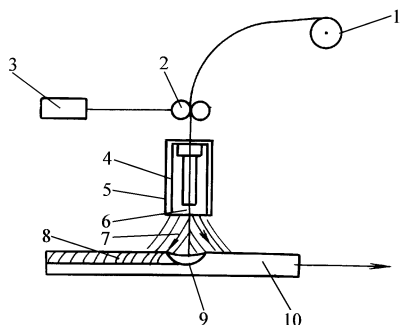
二氧化碳气体保护焊焊接过程示意图
